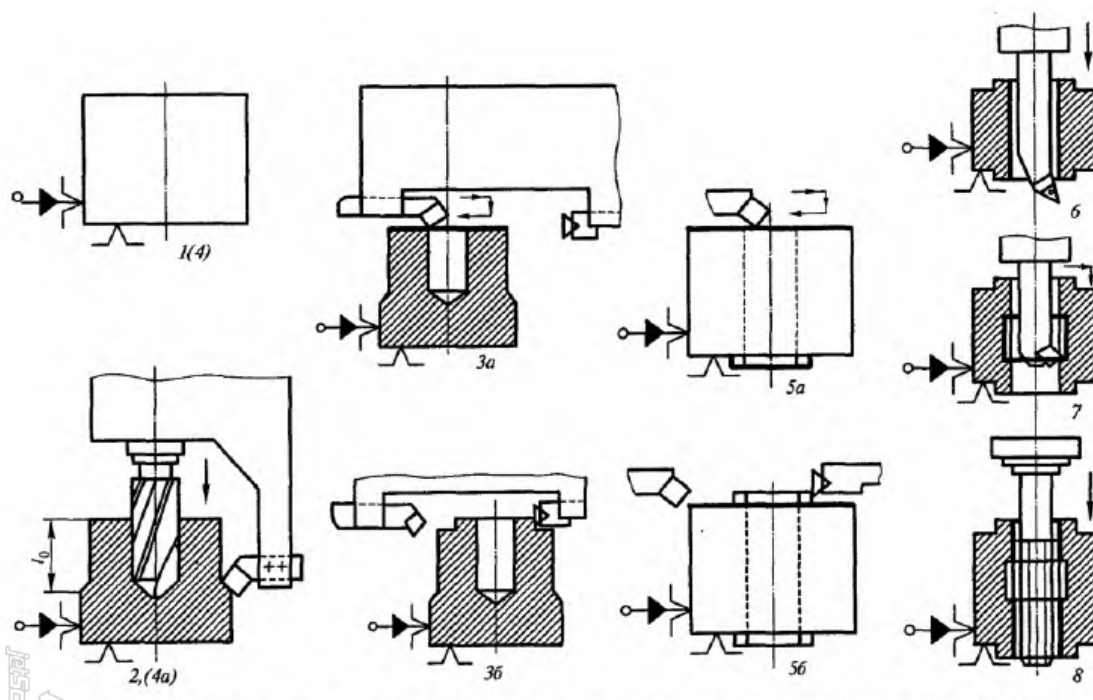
Схема токарного оброблення корпусу насадної розвертки на револьверному верстаті: 1 – намітка центра; 2 – свердлення отвору; 3 – наскрізне свердлення меншим діаметром; 4 – обточування зовнішнього діаметра; 5 – підрізка торця; 6 – чорнове розверстування кінцевого отвору; 7 – розточування виточки; 8 – чистове розверстування кінцевого отвору; 9 – оброблення фаски
